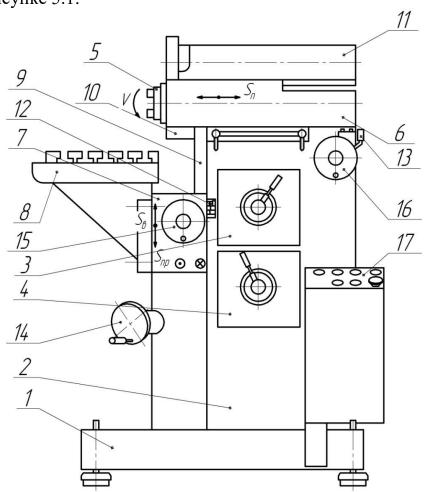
Общий вид широкоуниверсального горизонтально-фрезерного станка
